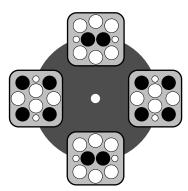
Rotor und Gehänge symmetrisch bestückt
